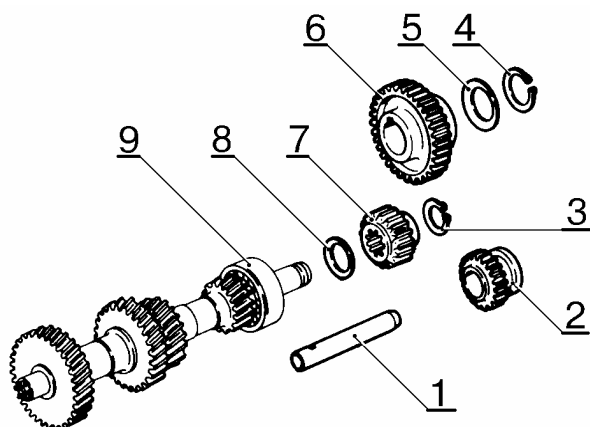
Детали задней передачи четырех-ступенчатой КП:
